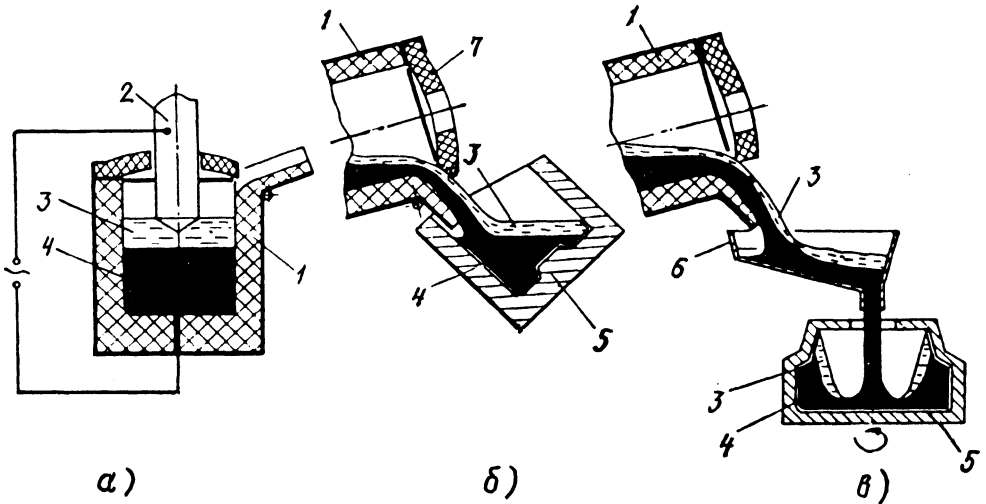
Схема ЭШП (а) и заливки металла в стационарную (б) и вращающуюся (в) формы: 1 - тигель; 2 - расходный электрод; 3 - жидкий шлак; 4 - жидкий металл; 5 - форма; 6 - промежуточный лоток; 7 - крышка-экран
